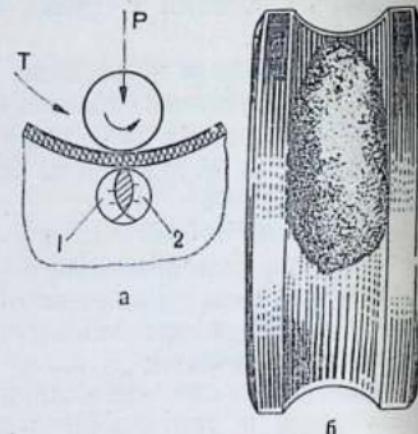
Схема усталостного изнашивания (а) и внешний вид кольца подшипника (б), претерпевшего усталостное изнашивание:
